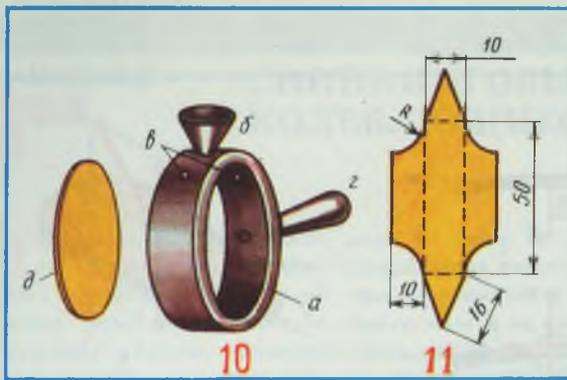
Алюминиевая форма для отливки блесен: а — корпус, сделанный из кольца высотой 1,5—2 см и толщиной стенки 4—5 мм; б — литник; в — отверстия для выхода газов  $\varnothing$  0,8—1 мм; г — ручка; д — боковые детали — 2 шт. (штампуются из листового металла толщиной 3—5 мм по форме лепестка блесны, а затем стачиваются для получения профиля приманки необходимого типа).
